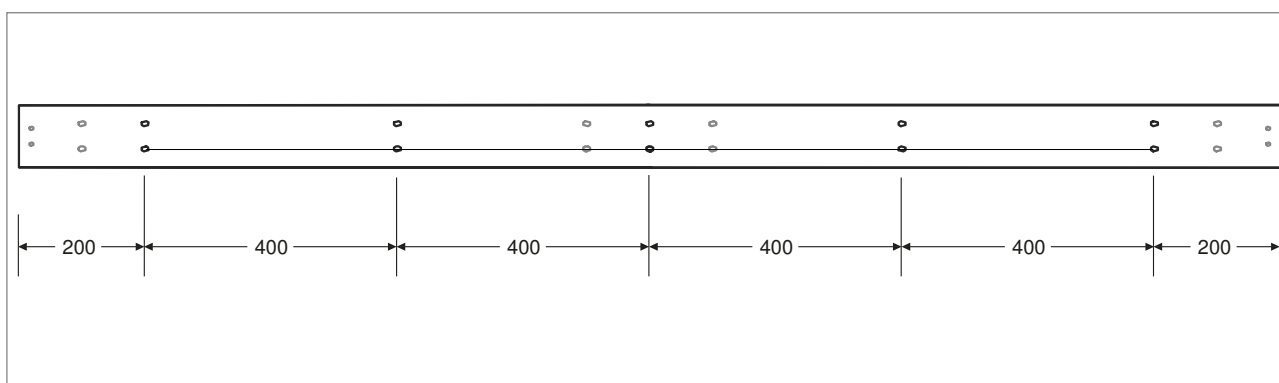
Configuration de perçage en cas de montage mural horizontal
